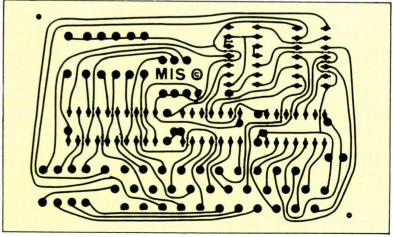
Circuit imprimé vu côté « soudures » (Ech. 1).
